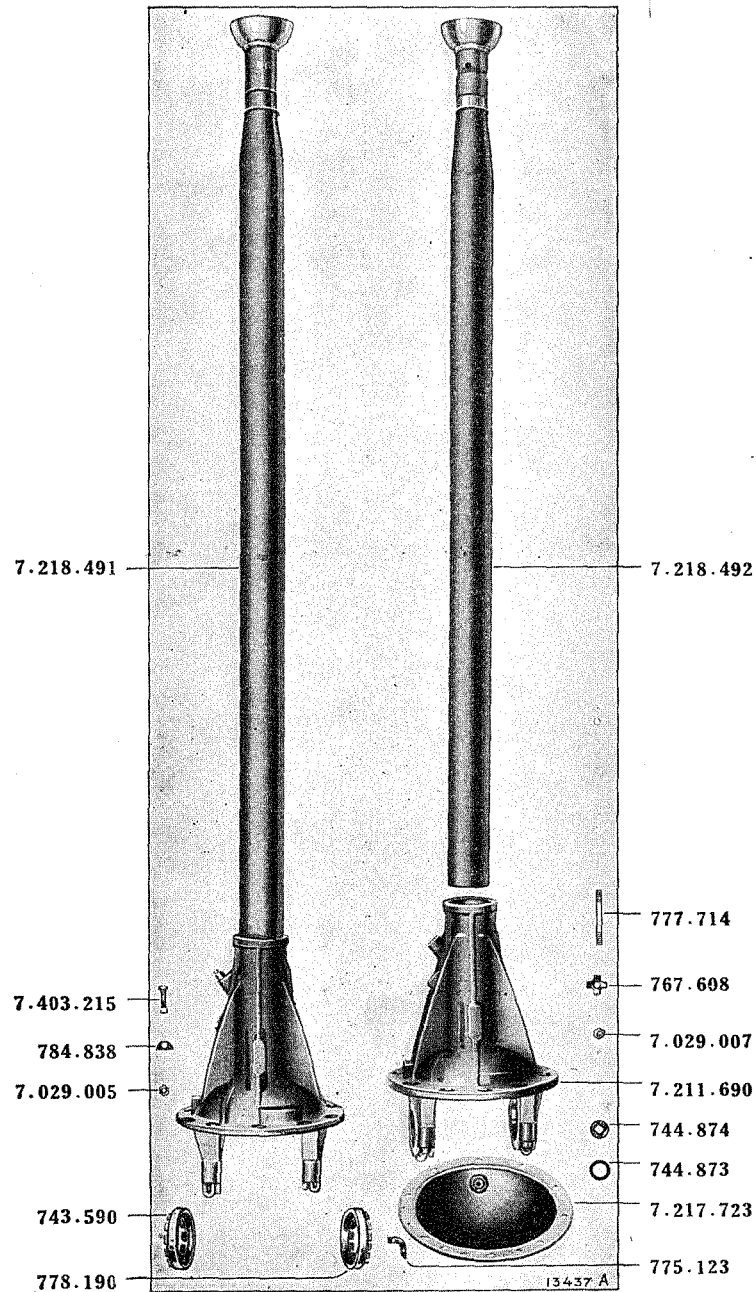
Couvercle, bouchons, tube de poussée et boîtier support de couple conique.
